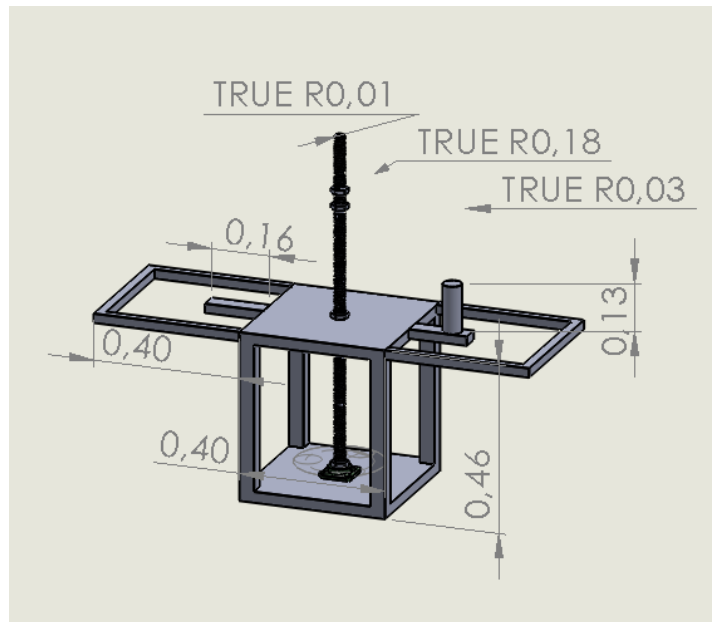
Vista CAD de soporte de turbina. (Fuente: autor)
